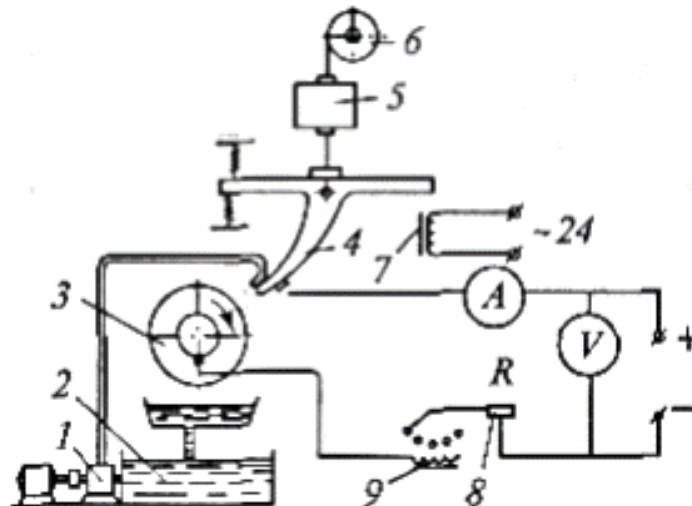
Схема установки для вібродугового наплавлення:
